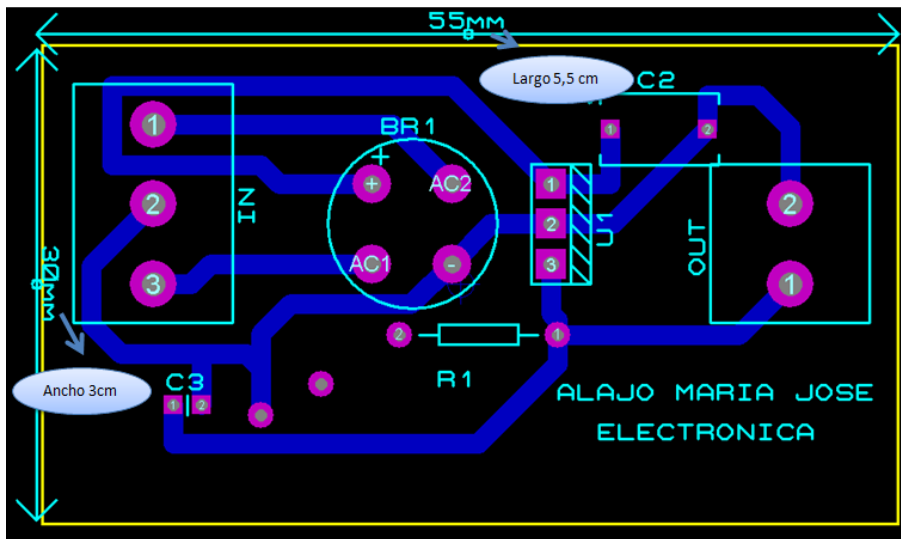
Dimensiones de la placa de la fuente de 5V
